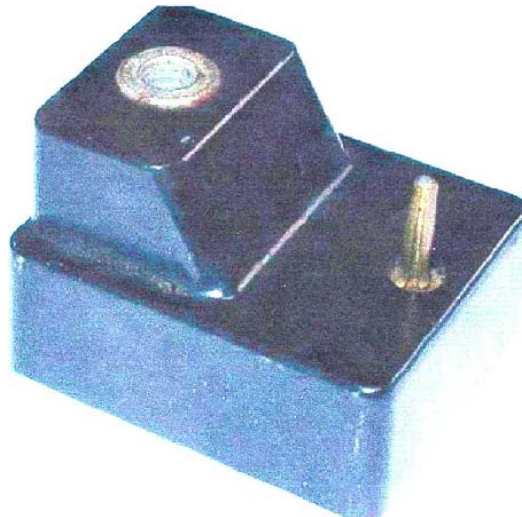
Steckerseitige Ansicht K.A. 15a
